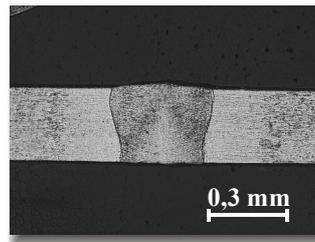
Querschliff einer Blindschweißung in ein 0,3 mm dickes Edelstahlblech ( $P_L = 230 W$ ,  $v = 3 m/min$ )
